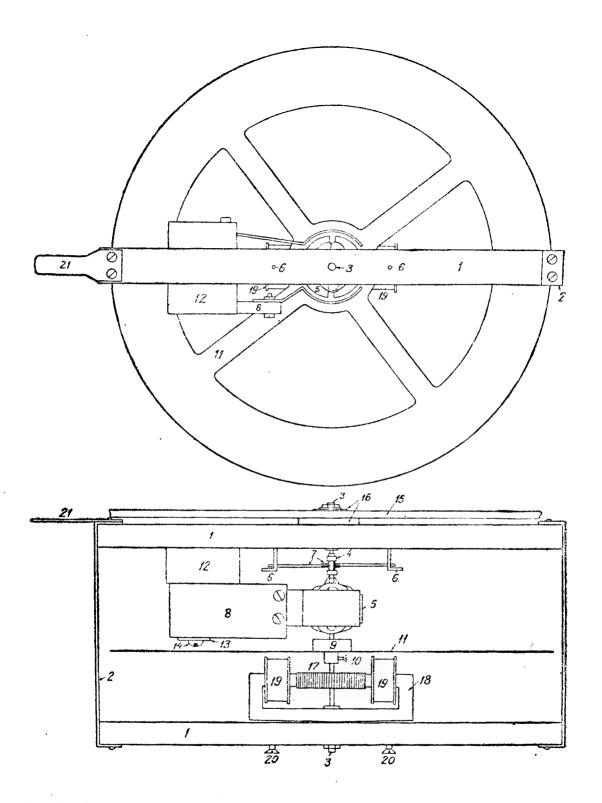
Сборка мотора первого варианта: 1— деревянные планки, 2— скобы, 3— контакты, 4— коллектор, 5— якорь, 6— щеткодержателн, 7— щетки, 8— магнит от УГ с полюсными наконечниками, 9— деревянная втулочка, крепящая диск, 10— шуруп, крепящий втулочку на оси, 11— диск Нипкова, 12— деревянная подкладка под магнит, 13— латунная пластинка, крепящая магнит, 14— винт, крепящий магнит к планке, 15—передняя стенка телевизора, 16— суконные шайбы для смягчения шума мотора, 17—колесо Лакура, 18—сердечник электромагнита, 19— катушка электромагнита, 20—шурупы для регулировки вазоров, 21— рычажок установки в рамку
